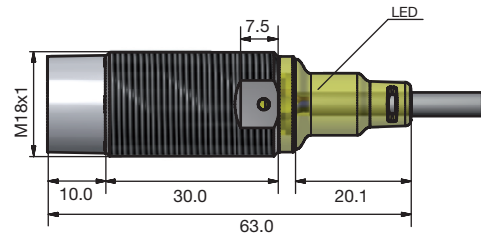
Kurze Ausführung, Nicht bündiger Einbau, Kabel
